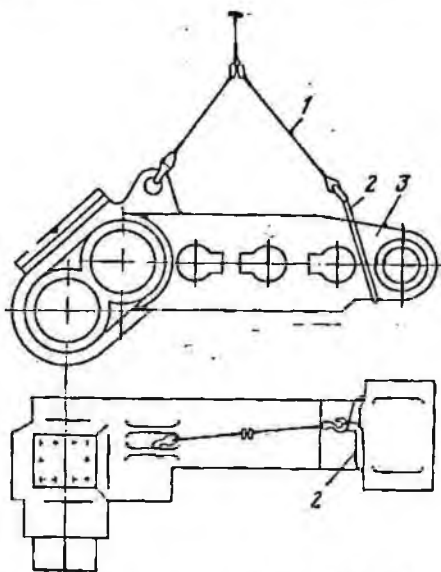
Строповка редуктора привода шнека комбайна КШЗМ:
